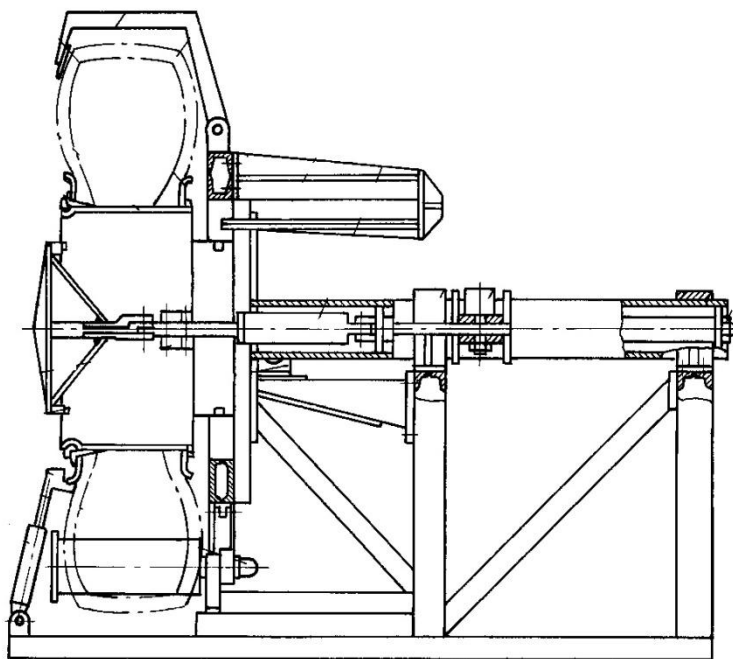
Стенд для монтажа и демонтажа пневматических шин
